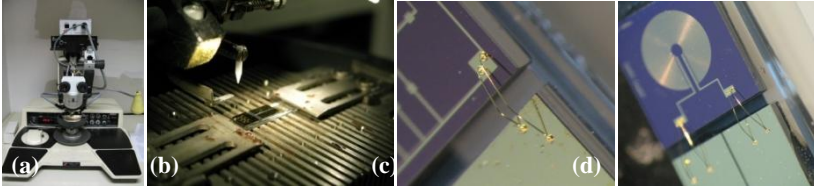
(a) Instrumentação para o bonding; (b) detalhe da agulha com o fio de Au e o chip pronto para ser soldado; e (c e d) resultados do bonding.
